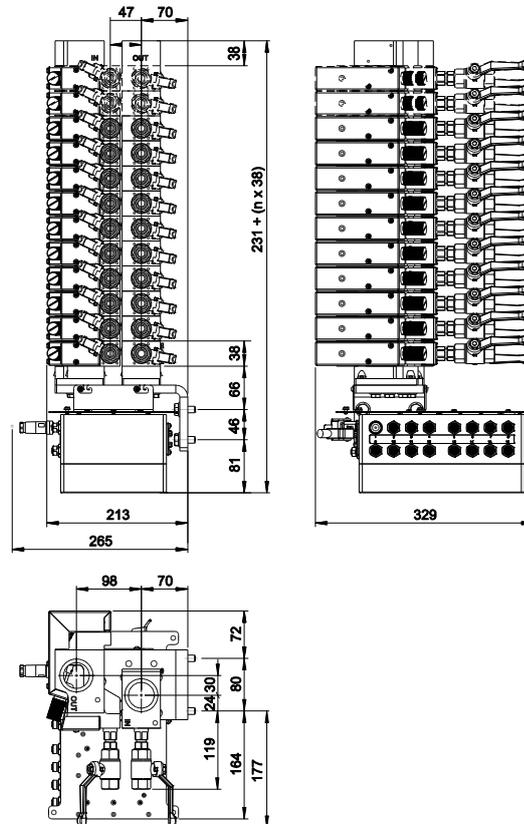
Размеры конструкции: автономный прибор (пример: НВ-FM160L16-12)
